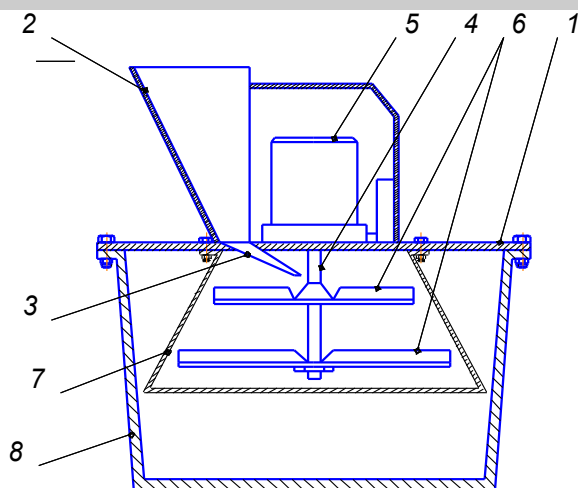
Устройство для дробления зерна: 1 – опора; 2 – загрузочная тара; 3 – направляющий канал; 4 – вал привода; 5 – электромотор; 6 – диски; 7 – обечайка ситовая; 8 – отражательный элемент
